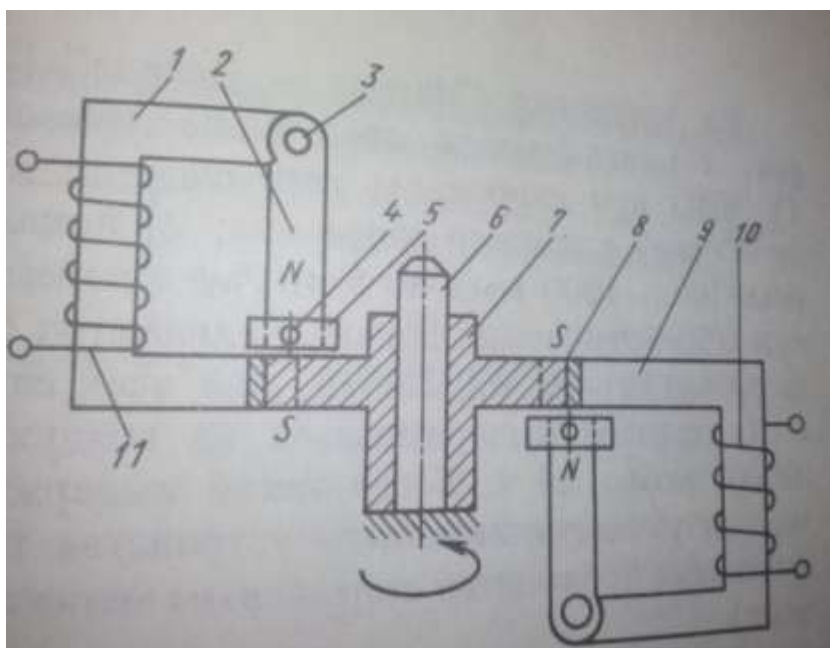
Схема приспособления для магнитно-импульсной обработки зубчатых колес
